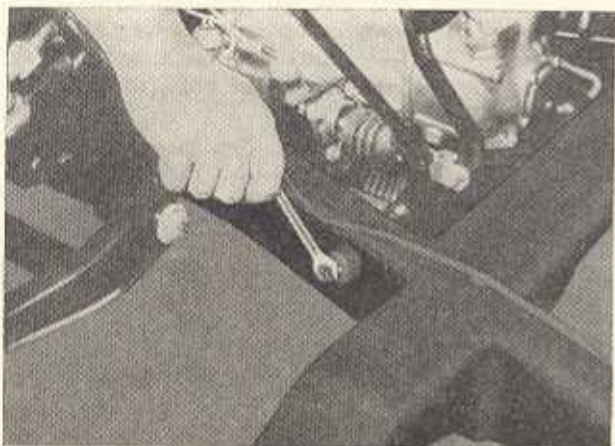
Heraus-schrauben der Sechskantschraube M 6 an der Fußhebelwelle
